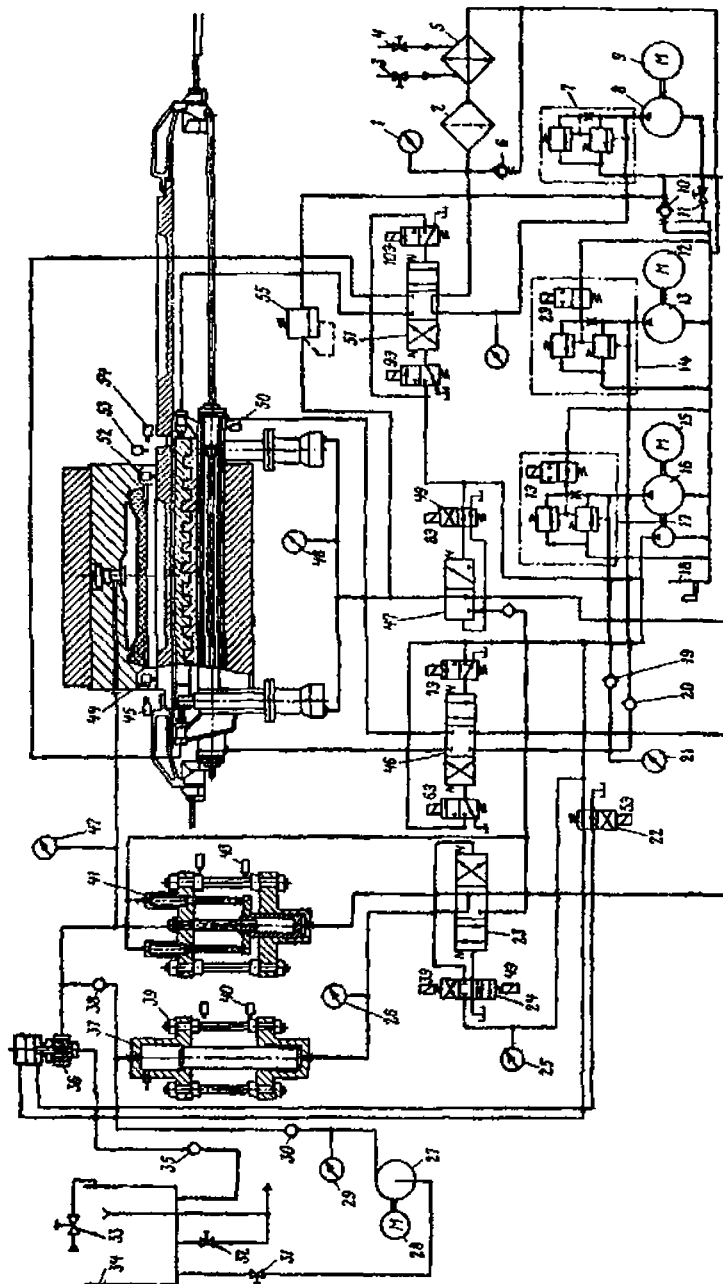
Гидросхема прессы для штамповки резиной усилием 160000 кН
